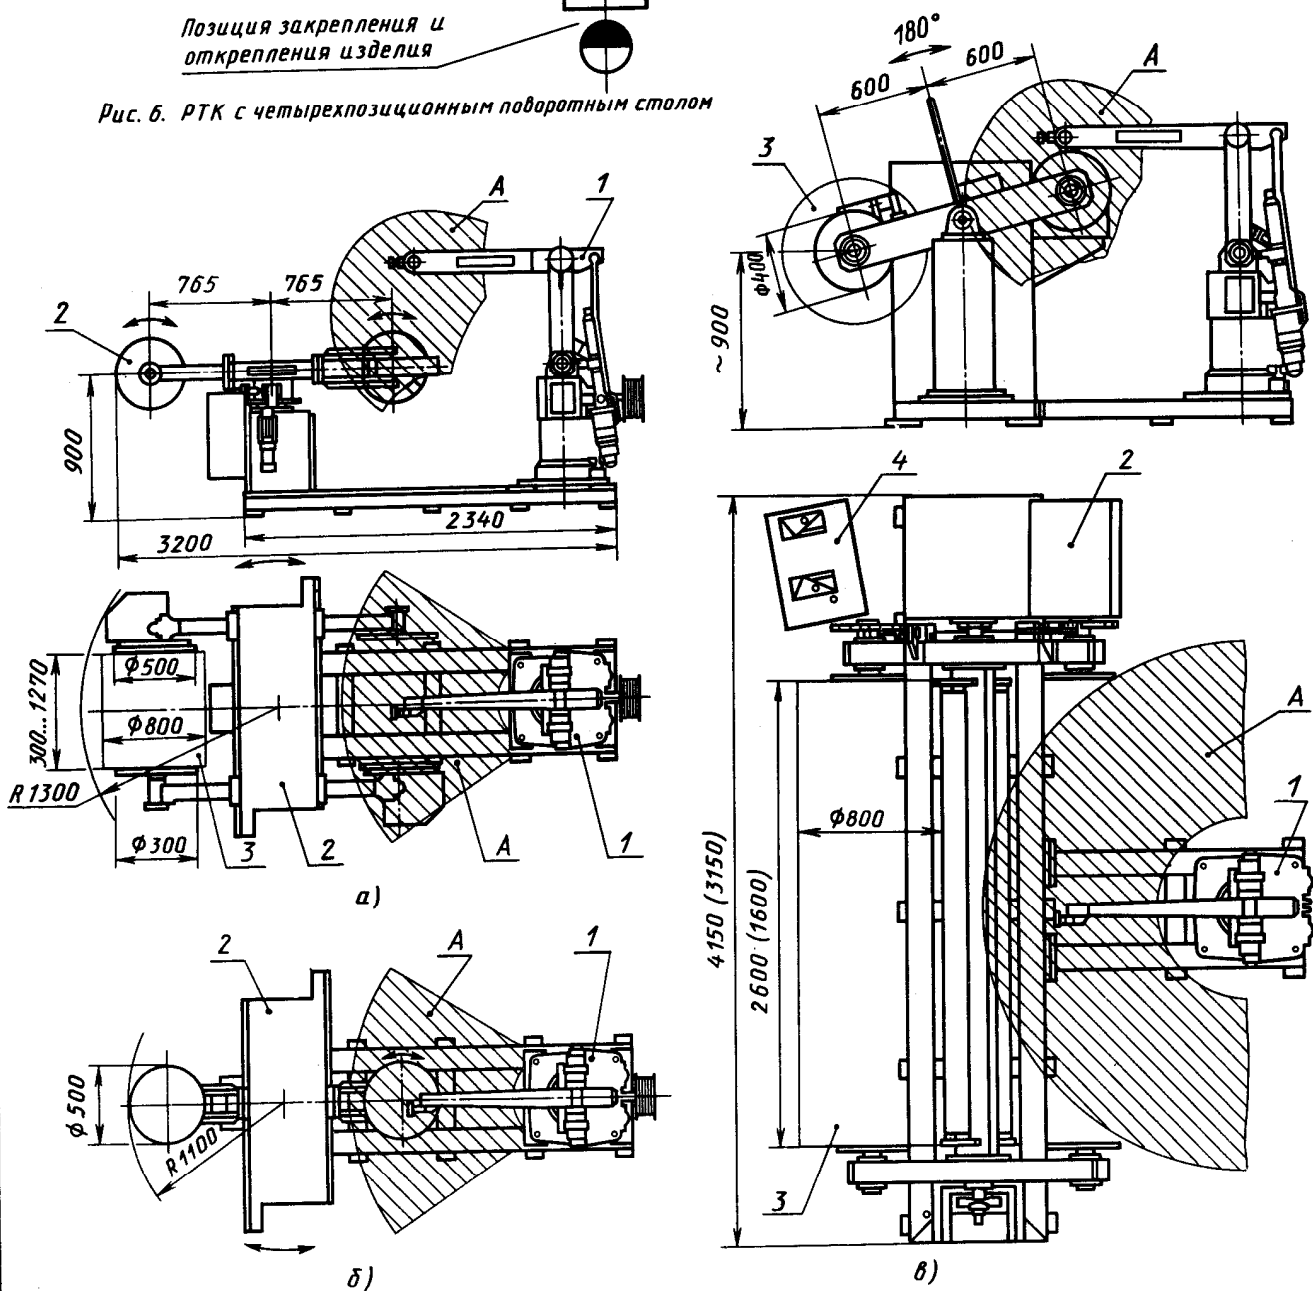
РТК для дуговой сварки с двухпозиционными поворотными приспособлениями
